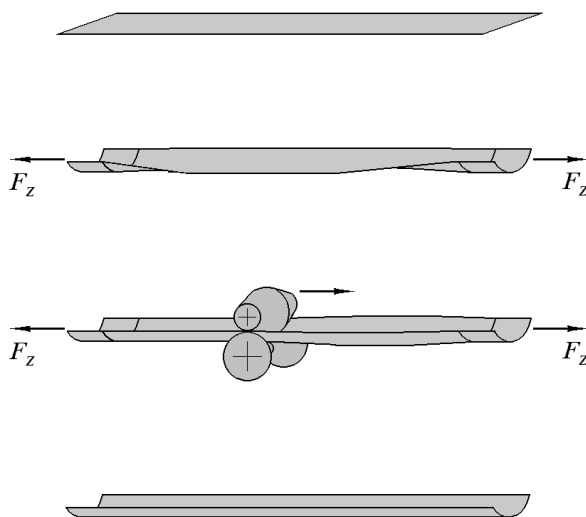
Способ изготовления профилей с продольным растяжением по [35]
